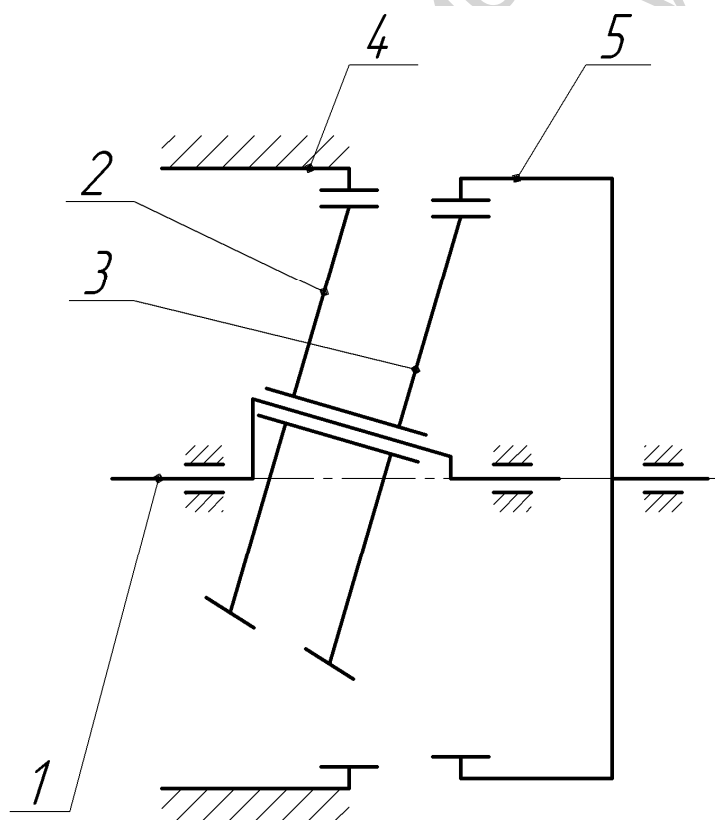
Структурная схема планетарной прецессионной передачи с зубьями сателлита, выполненными на внутренней цилиндрической поверхности
